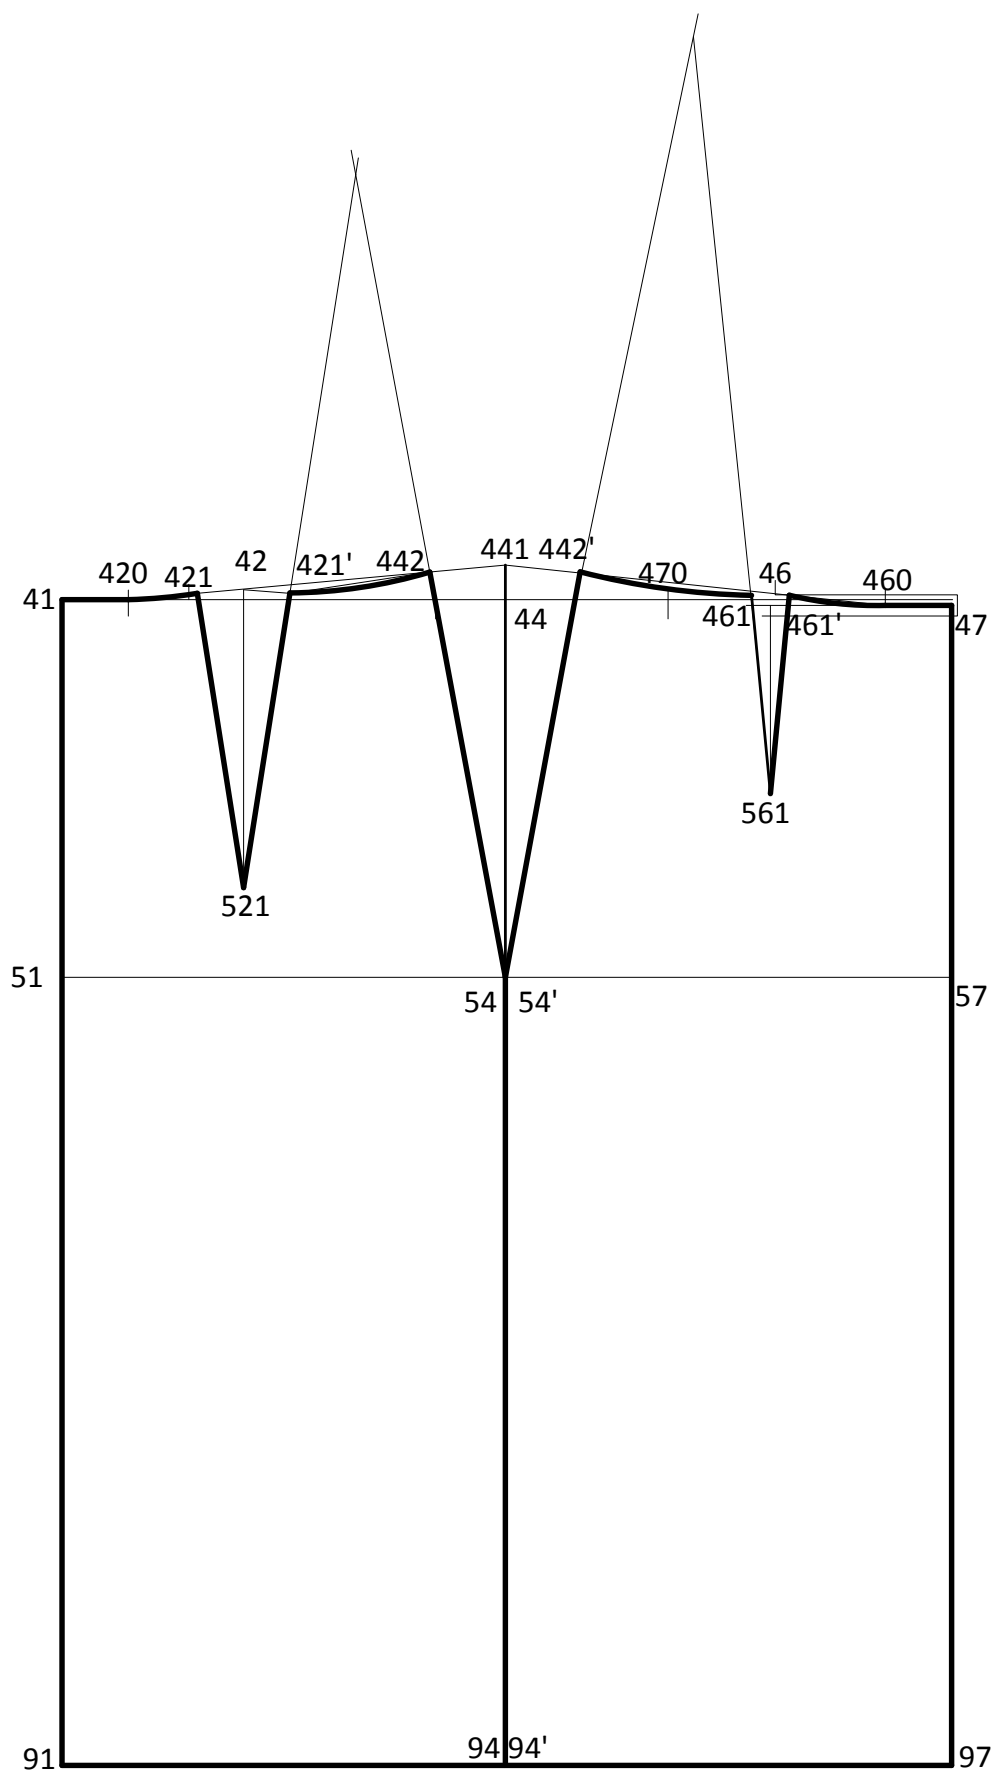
Чертеж базовой конструкции прямой юбки (170-84-88)
